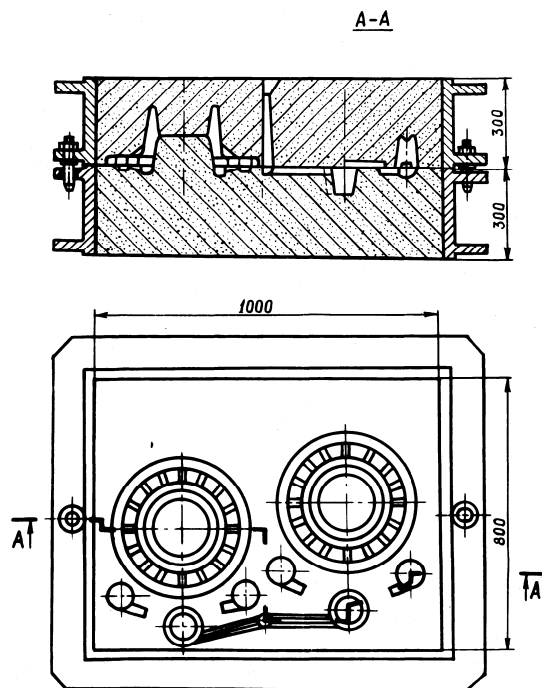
Ливарна форма для виготовлення виливка «Картер планетарного редуктора»
